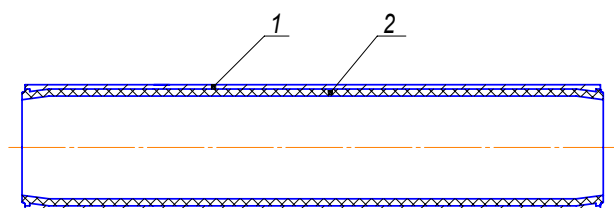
Разрез цилиндрического корпуса с покрытием: 1 – металлическая арматура; 2 – резиновое покрытие
